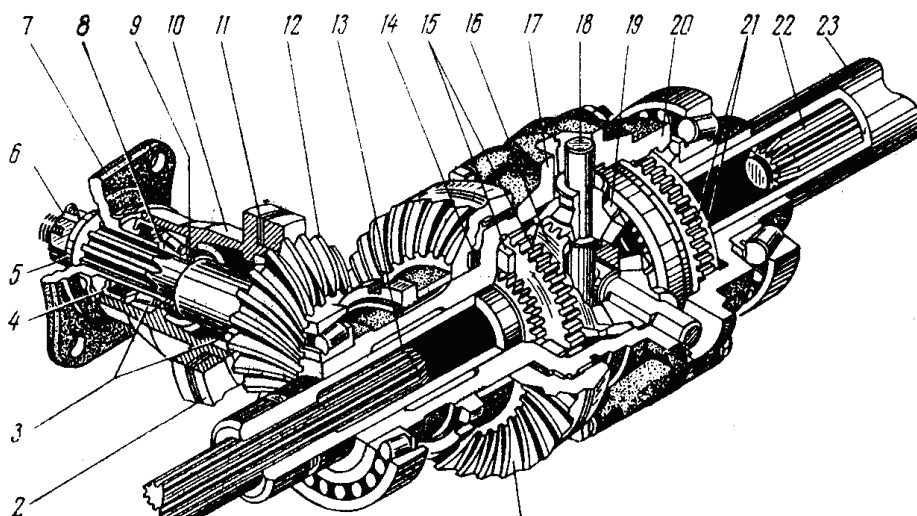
Главная передача переднего ведущего моста. 1 — ведомая шестерня главной передачи; 2 — корпус переднего моста; 3 — подшипники; 4 — са льяник; 5 — шайба; 6 — гайка; 7 — фланец карданного вала; 8 — маслоотража тель; 9 — рег улировочные кольца; 10 — стакан шестерни главной передачи; 11 — прокладки; 12 — ведущая шестерня главной передачи; 13 — правая полуось; 14 — прокладки; 15 — фрикционные диски дифференциала; 16 — нажимная чашка; 17 — корпус дифференциала; 18 — ось сателлитов; 19 — сателлит; 20 — крышка корпуса дифференциала; 21 — ведомый и ведущий фрикционные диски дифференциала; 22 — левая ведущая полуось; 23 — полуосевая шестерня
